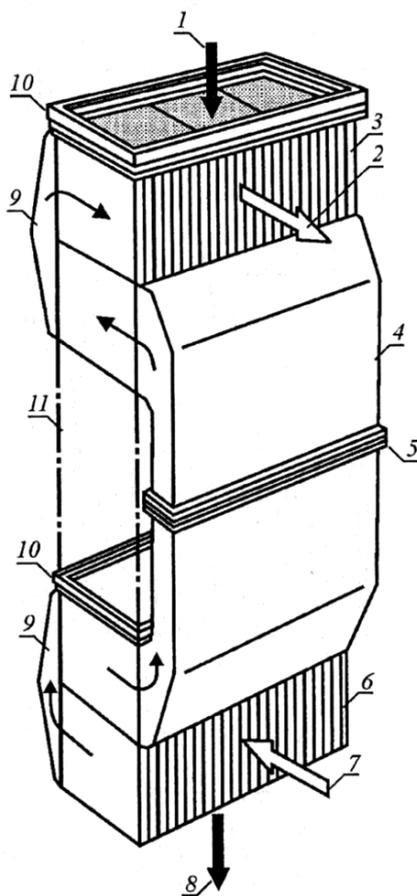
Схема трубчатого двухъярусного воздухоподогревателя:
